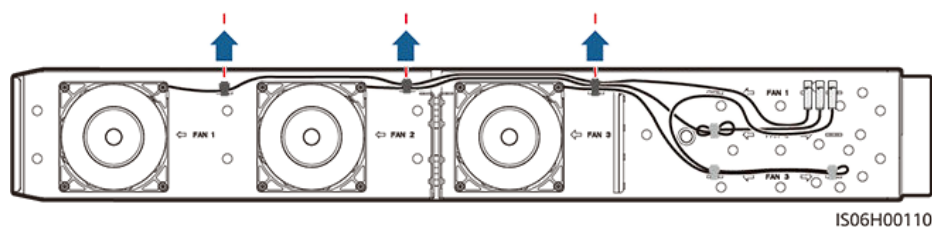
Extracción de la bandeja de ventiladores (2)
